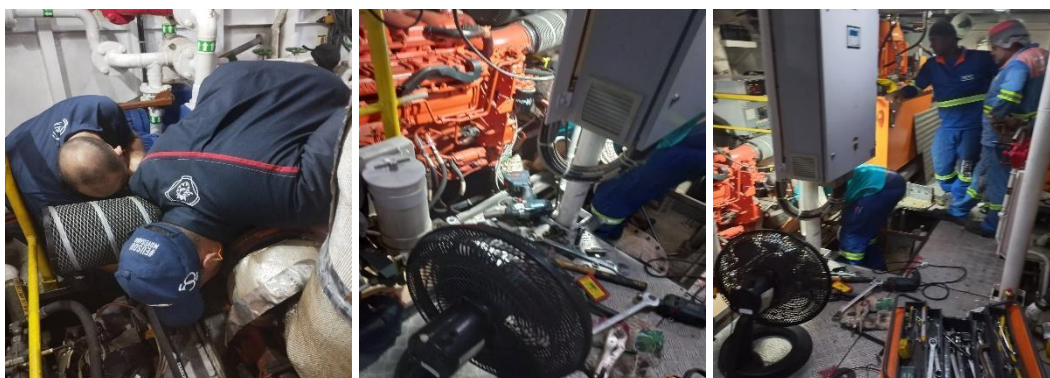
Serviço de reparo de motor pela empresa representante do fabricante do motor.
